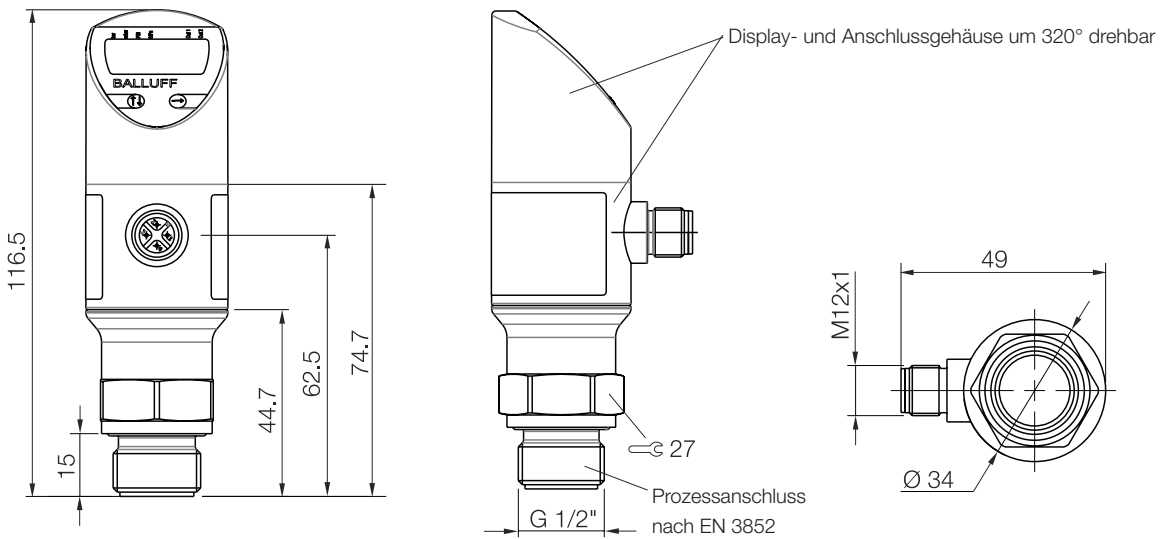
Maßzeichnung frontbündiger Drucksensor bis 50 bar
